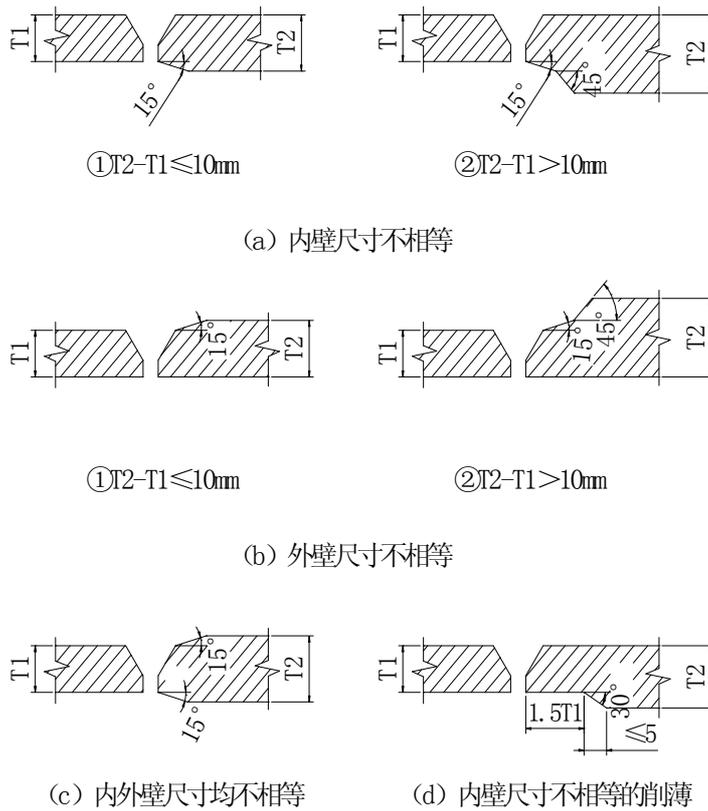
不等厚对接焊件坡口加工尺寸
